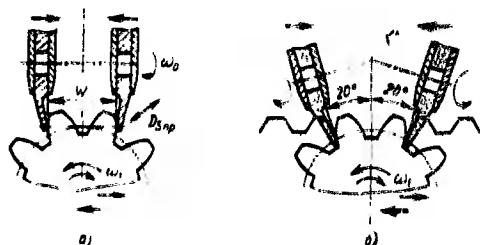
Схема зубошлифования тарельчатыми кругами
